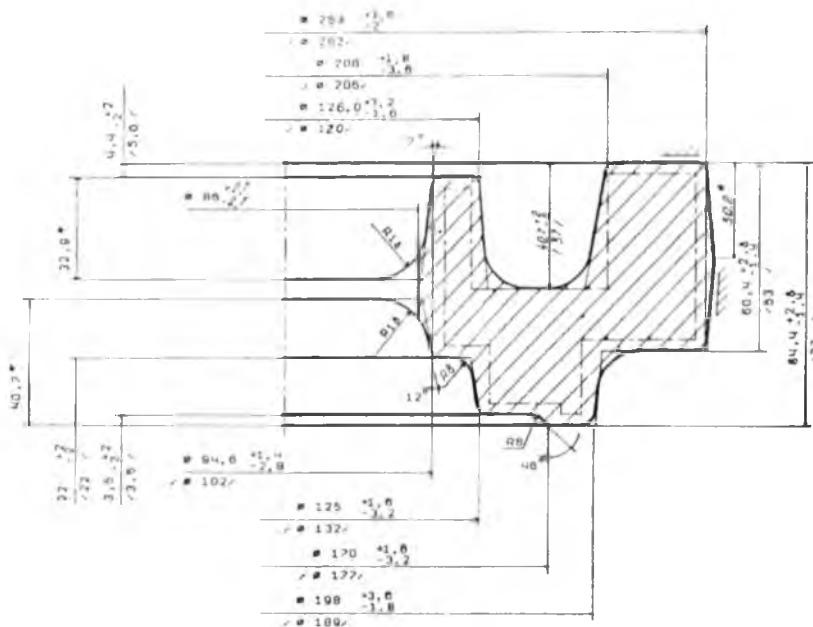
Чертеж поковки, полученный на графопостроителе в САПР
